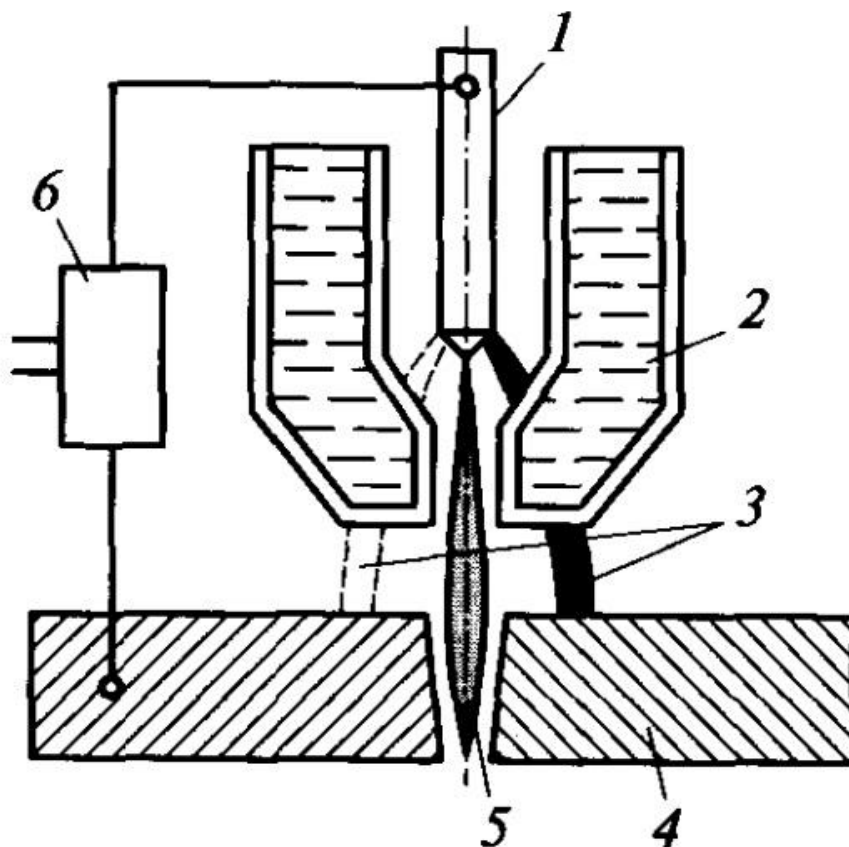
Схема плазменно-дуговой сварки [17]
